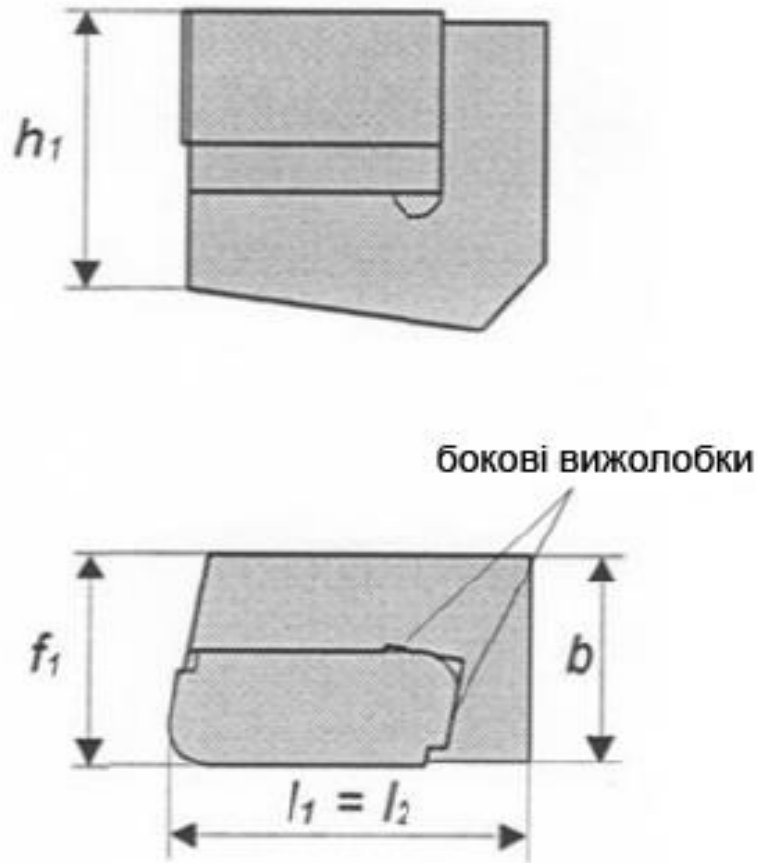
Різцеві блоки фірми «Sandvik Coromat» з боковими вижолобками для кріплення тангенційних пластин
